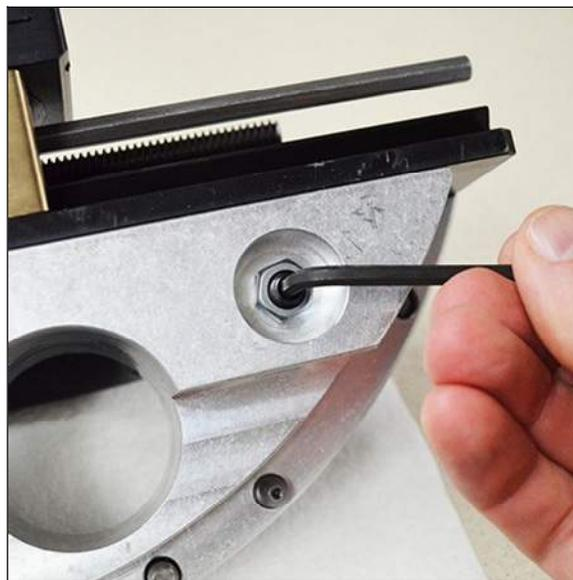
DESSERRER LA VIS DE BLOCAGE DE LA GLISSIÈRE (FF1200 ILLUSTRÉE)
